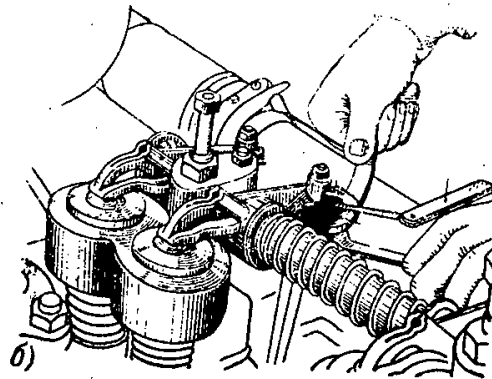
Регулировка зазоров клапанов и штанг декомпрессора
